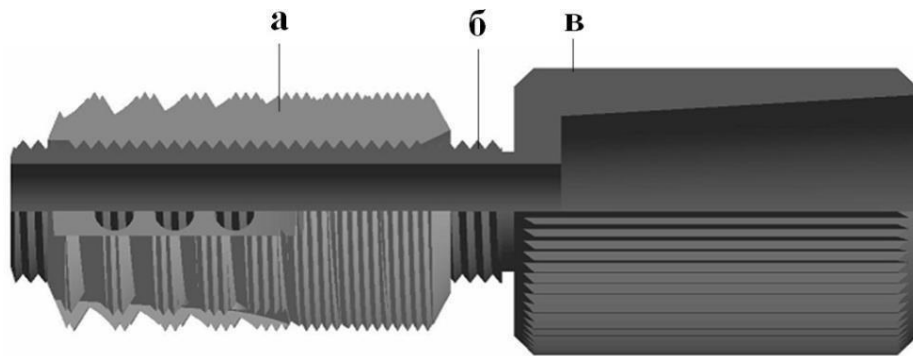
Штуцер конструкции автора для канюли шприца и подвода через имплантат-имитатор костно-пластического материала: а – имплантат-имитатор конструкции автора; б - полый резьбовой стержень штуцера в - штуцер для канюли шприца
